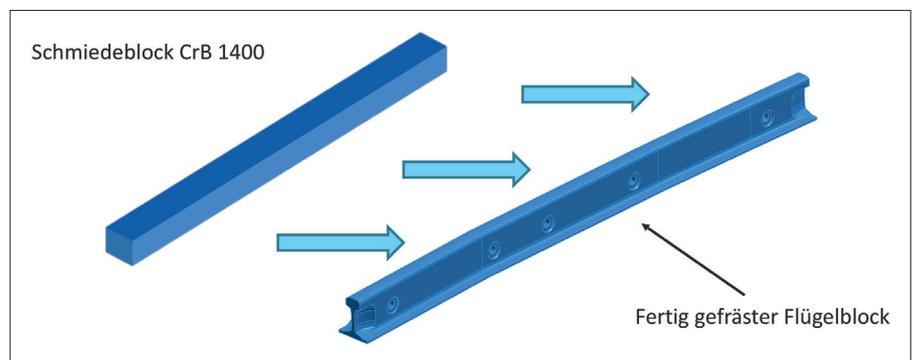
Vom Rohblock zum fertig gefrästen Flügelblock
